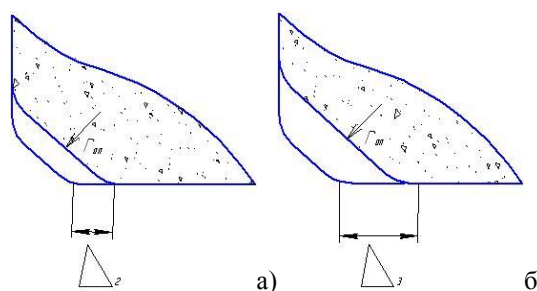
Формоизменение рабочей поверхности шлифовального круга при шлифовании фасок резьбонакатного ролика
